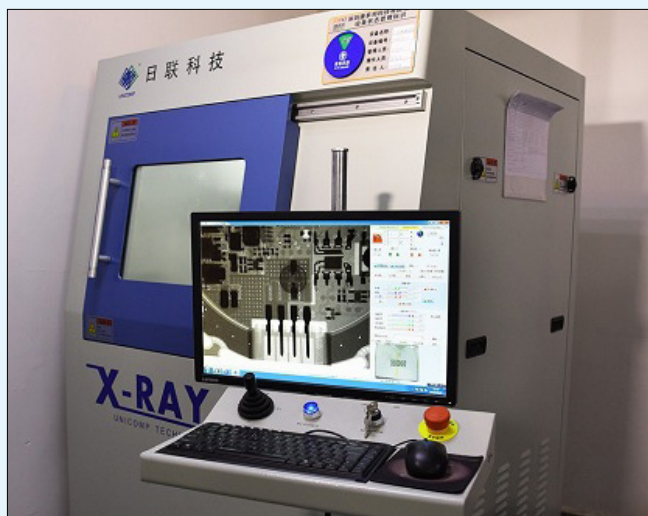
Macchina X-RAY (fonte: [www.pcbway.com](http://www.pcbway.com))
